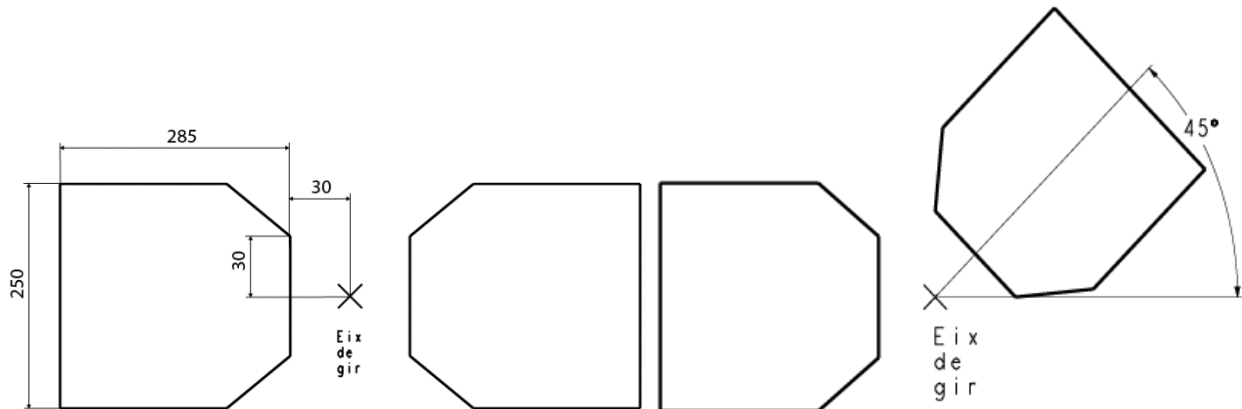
Posició recta (esquerra) i posició extrema (dreta) del conjunt de direcció del vehicle
